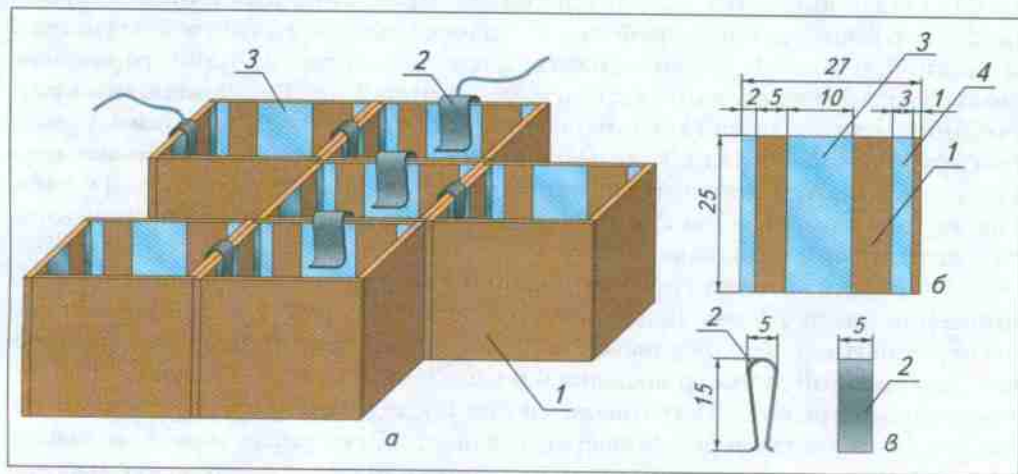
Внешний вид и устройство конструктора «Радиокубики»: а — внешний вид; б — панель из стеклотекстолита; в — пружинящая соединительная скобка
